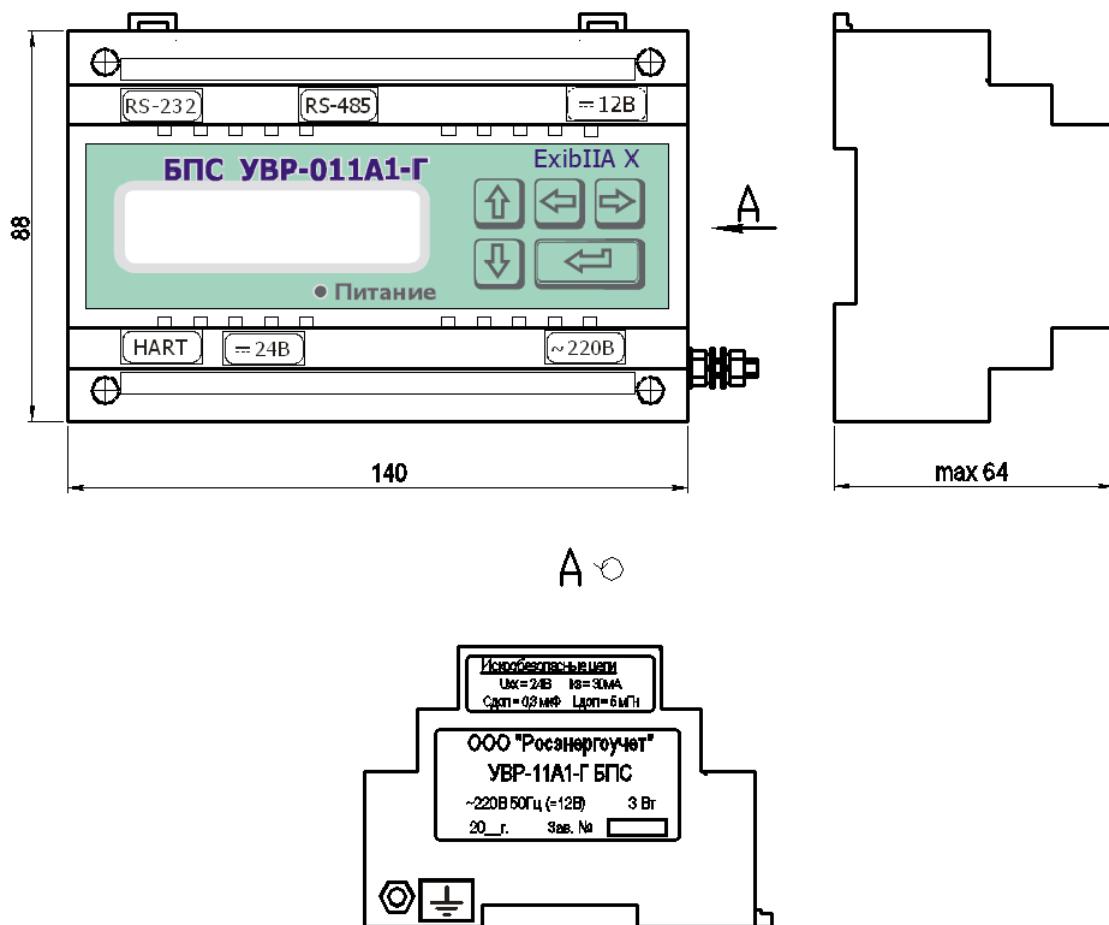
Внешний вид, габаритные и установочные размеры БПС
